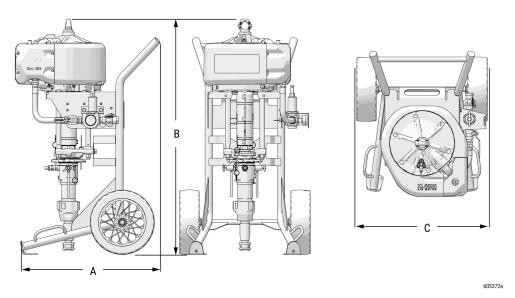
Dimensões dos Conjuntos de equipamento de pintura em carrinho
